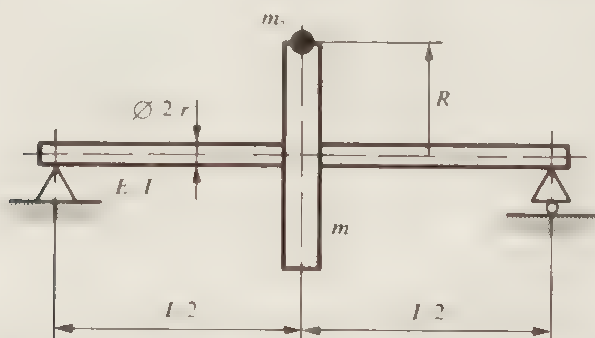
Arbre de machine supportant un disque avec balourd
